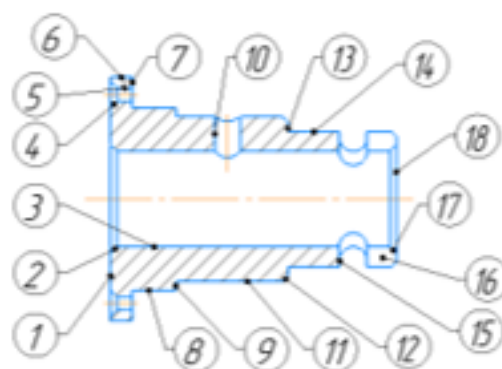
Технологічна розмітка поверхонь деталі
